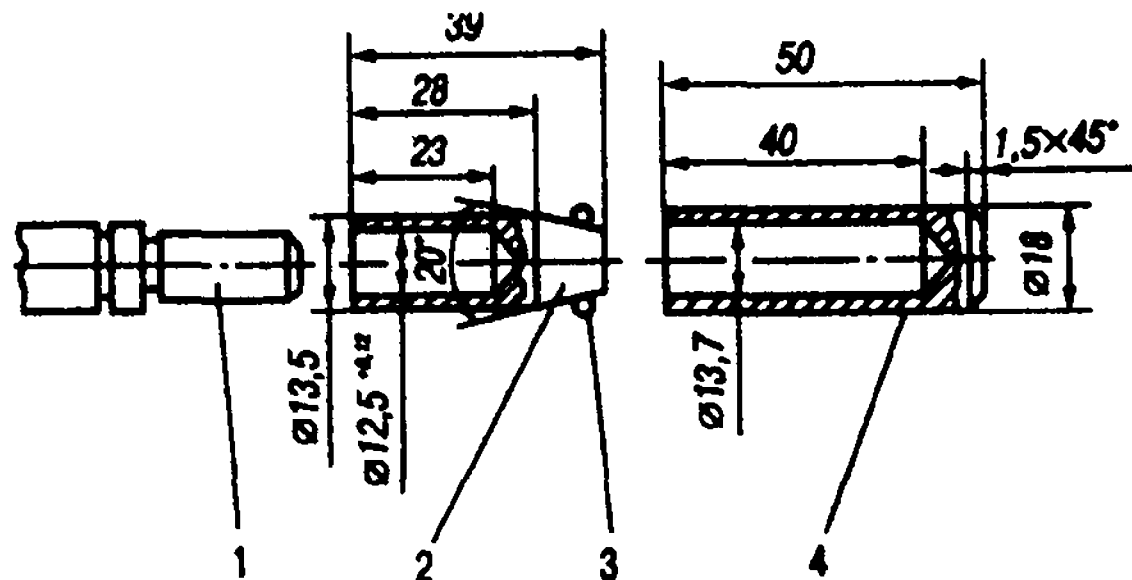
Приспособление для одевания пружинного кольца: 1 - вал якоря, 2 - втулка направляющая, 3 - кольцо пружинное, 4 - толкатель
